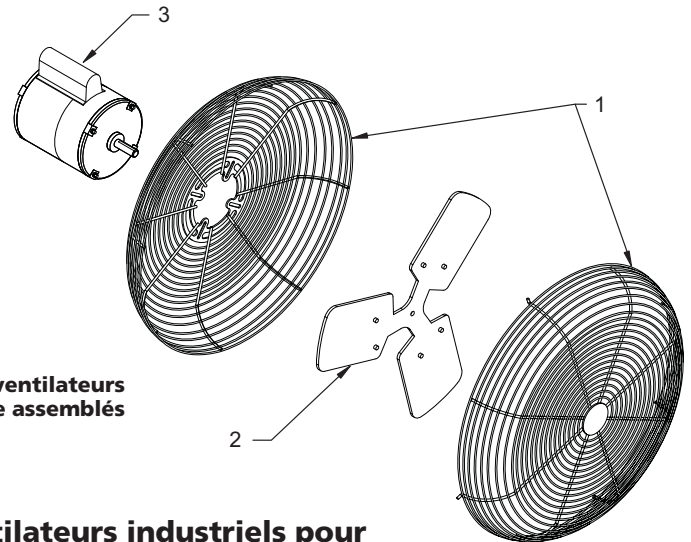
Pièces de rechange pour ventilateurs industriels pour haute température ambiante assemblés
